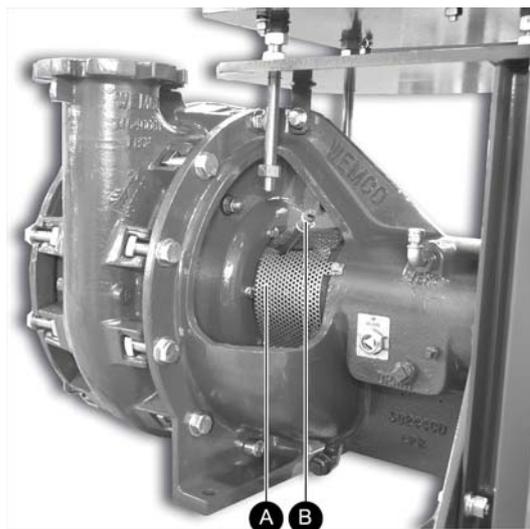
Dépose de la grille de protection (A) et du tube d'arrosage de tresses (B).
